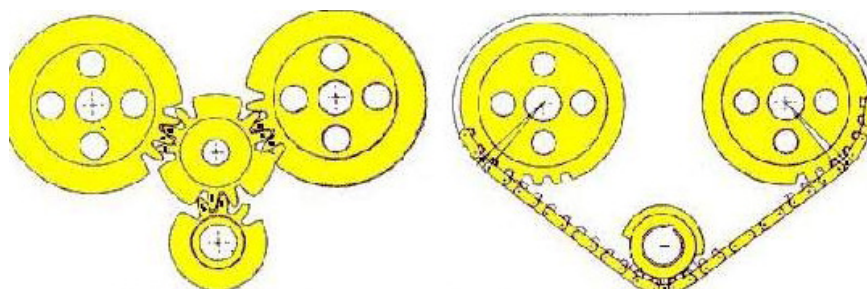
Sistema de transmissão por engrenagens. Fonte³³
